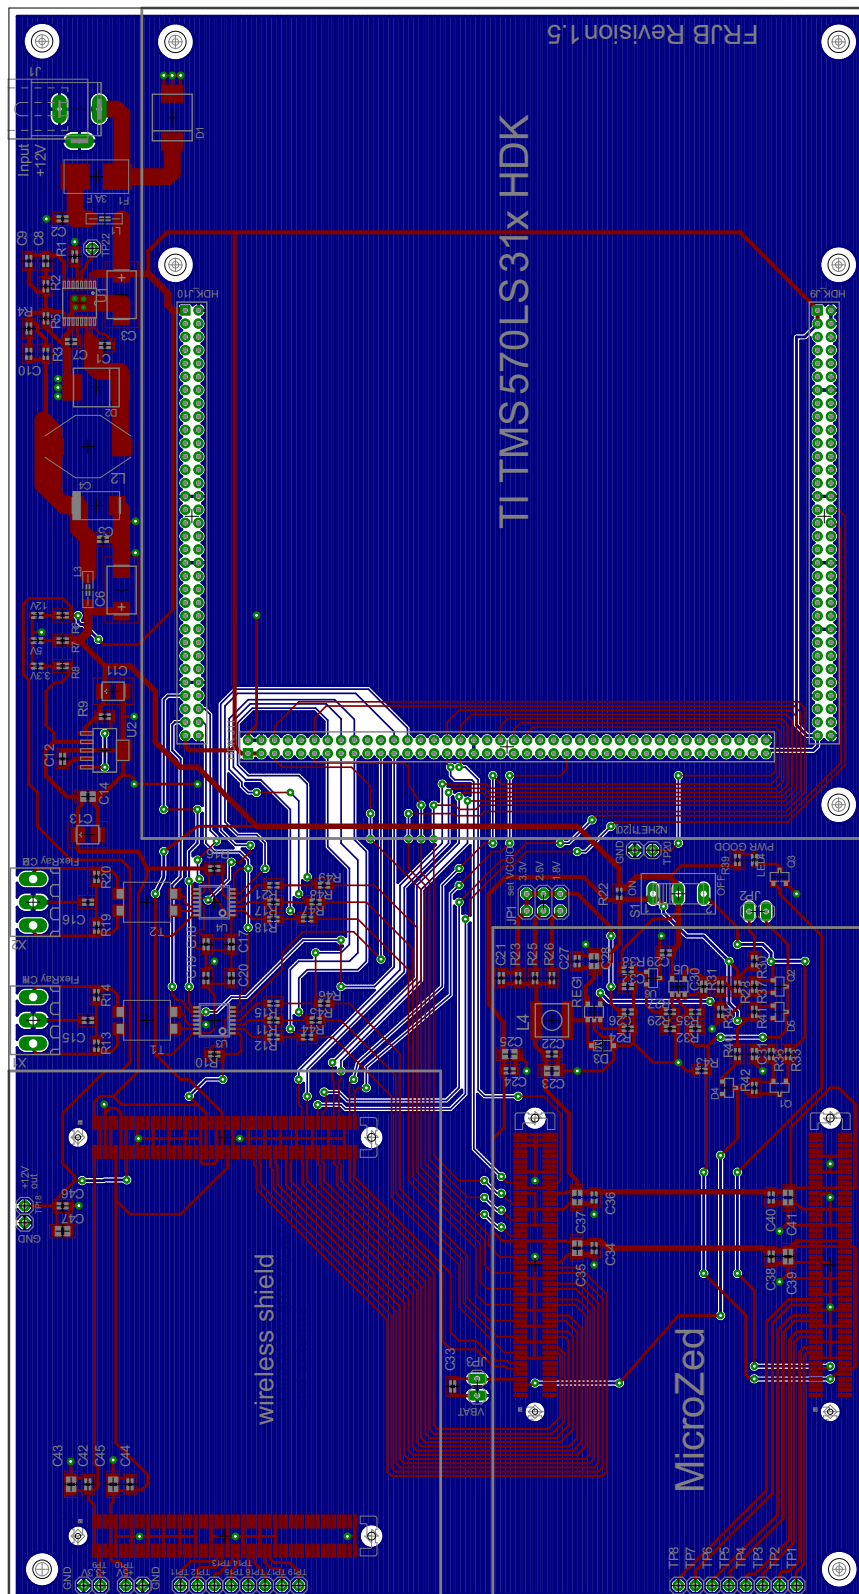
PCB Layout der Evaluierungsplattform Revision 1.5 (realisierter Prototyp)
